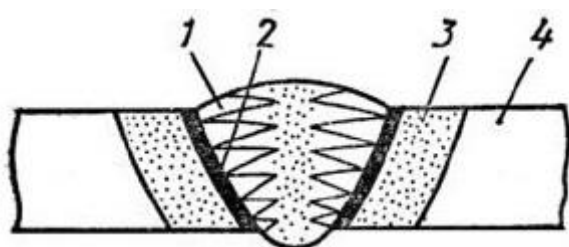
Схема сварного соединения: 1 — сварной шов; 2 — зона сплавления; 3 — зона термического влияния; 4 — основной металл; 1,2,3 – сварное соединение
